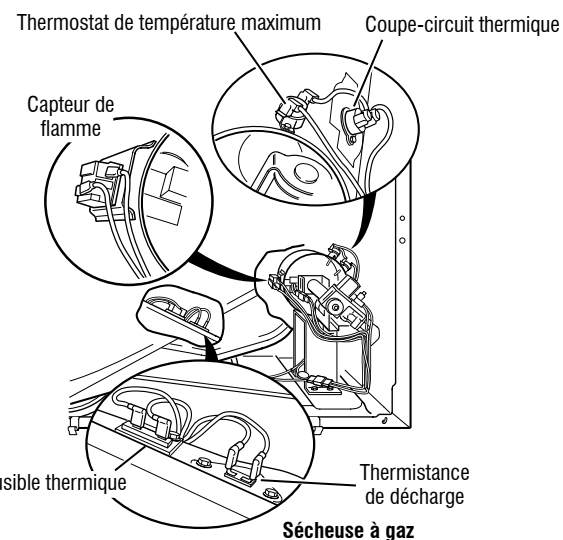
Composants thermiques, sècheuse à gaz, vue de face.
